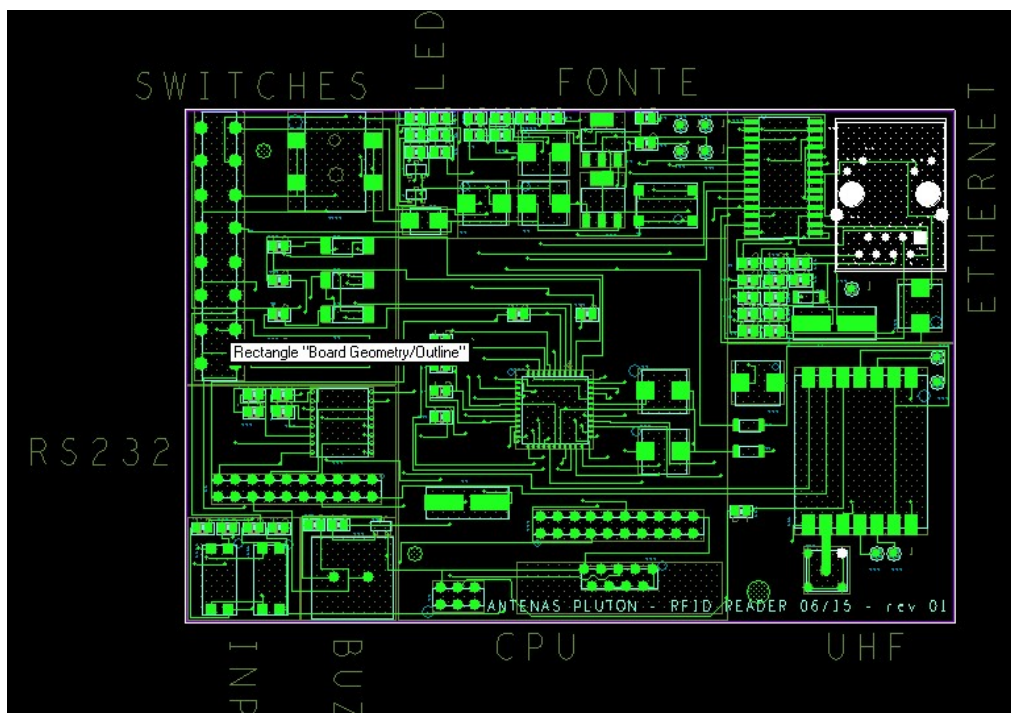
IMAGEM DA PCB LAYER BOTTOM
